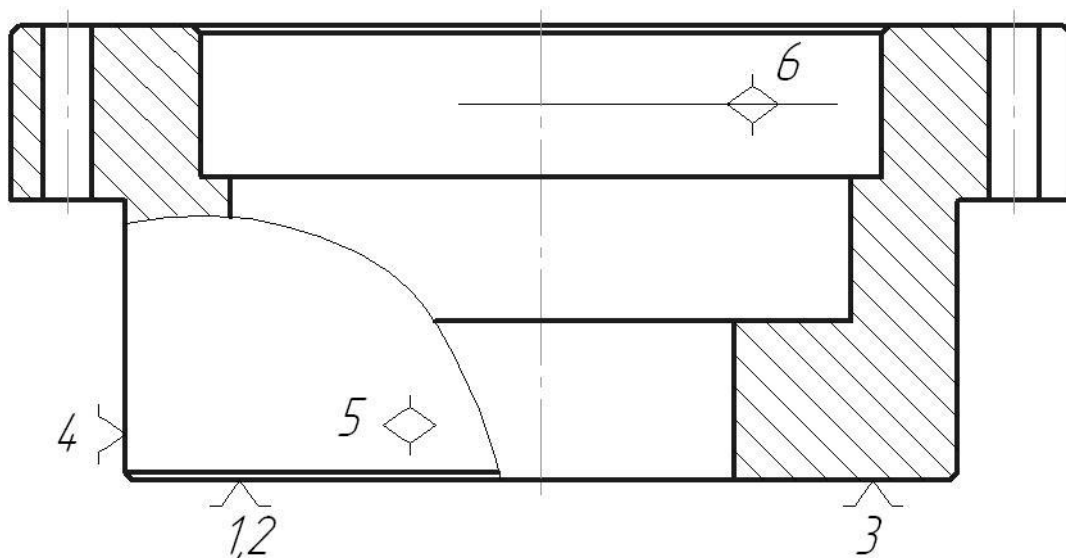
Схема базирования заготовки с установочными элементами приспособления
